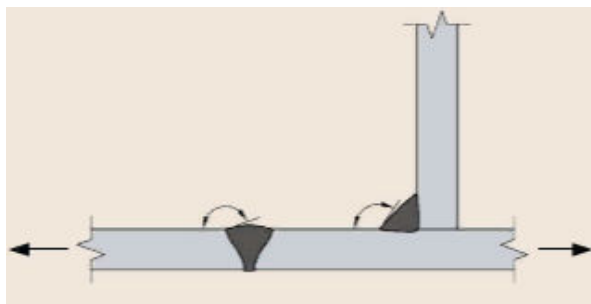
Поперечное сечение при угловом и стыковом сварных швах
